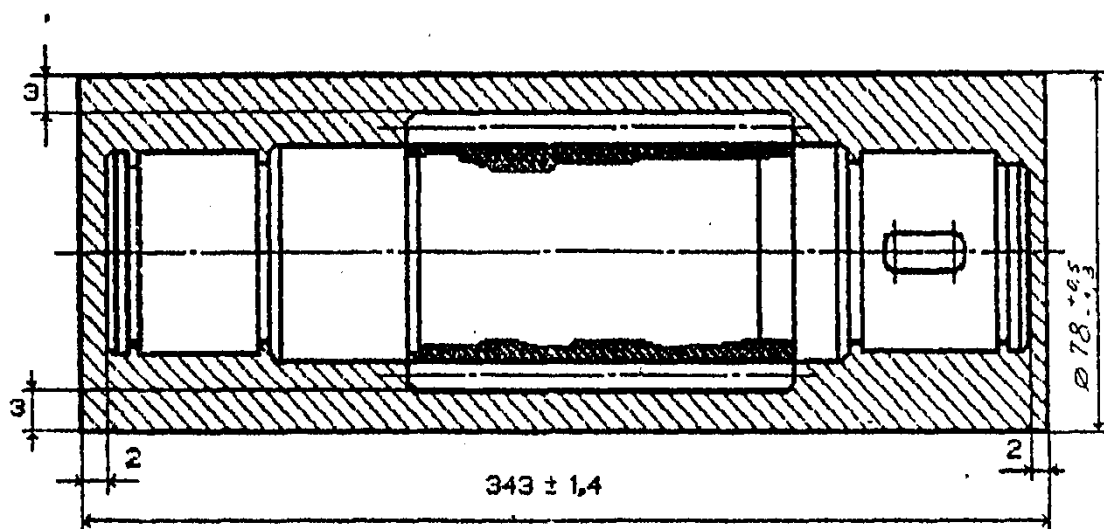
Заготовка из круглого проката для детали «вал-шестерня»
